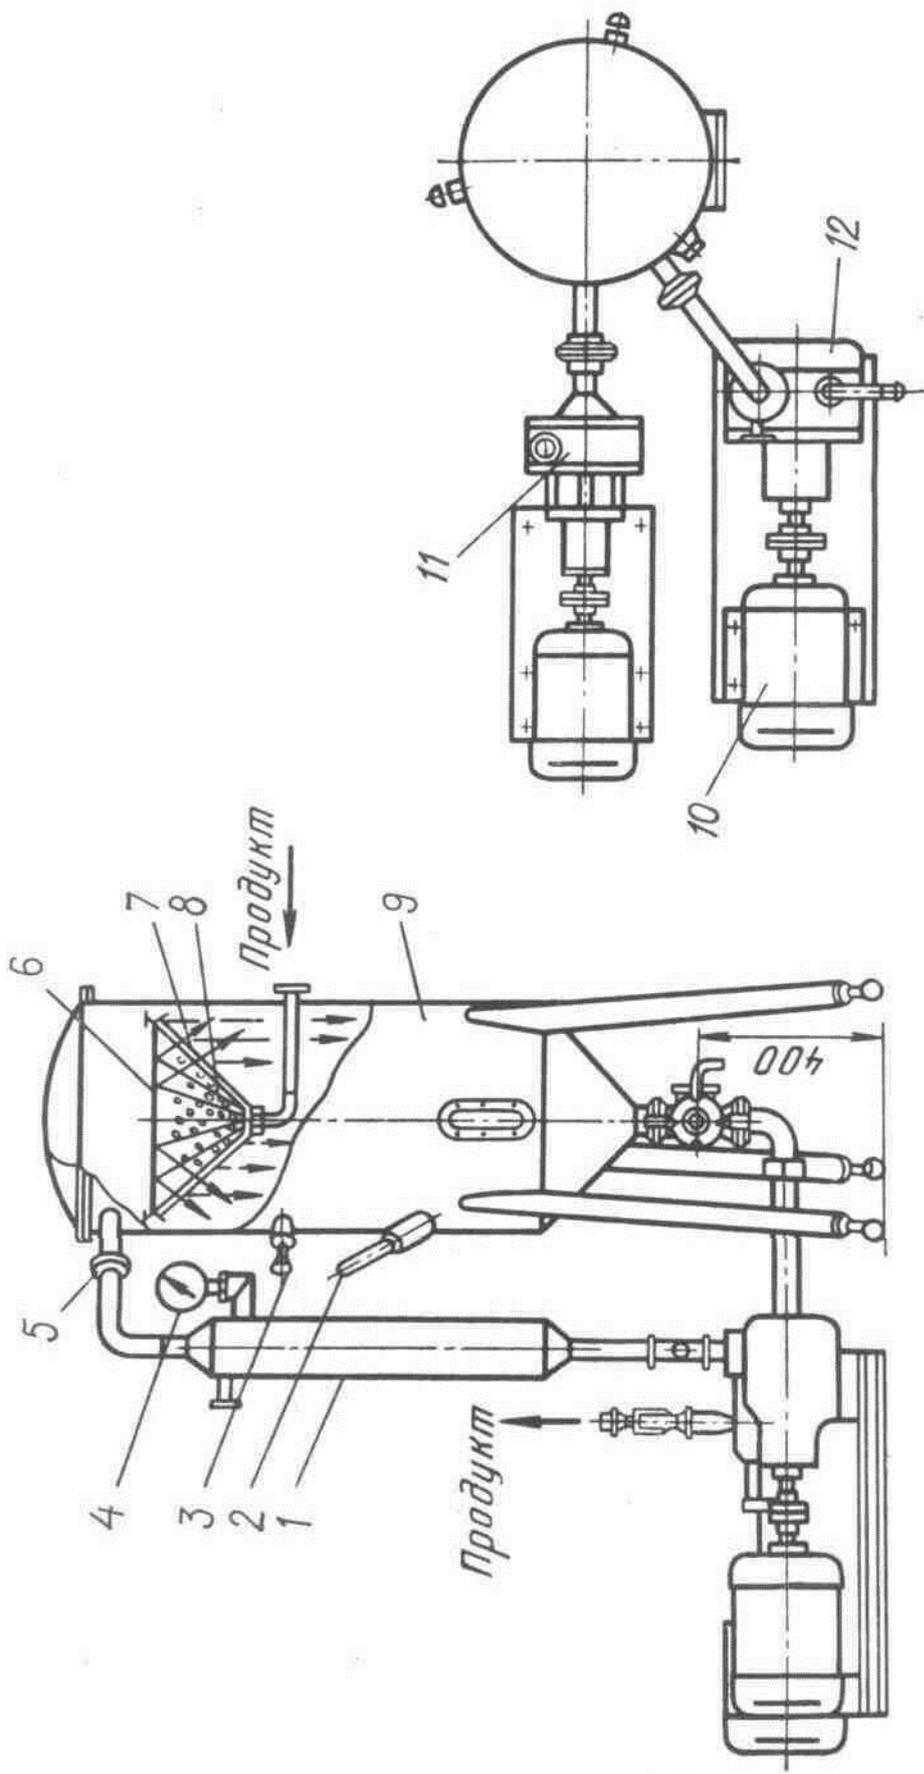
Установка для термовакуумной обработки молока и сливок: 1 – конденсатор; 2 – термометр; 3 – воздушный клапан; 4 – вакуумметр; 5 – обратный клапан; 6 – крышка-отражатель; 7 – перфорированная камера; 8 – пакет инертных шарообразных тел; 9 – камера для термовакуумной обработки (вакуум-дезодорация); 10 – электродвигатель; 11 – насос для продукта; 12 – вакуум-насос
